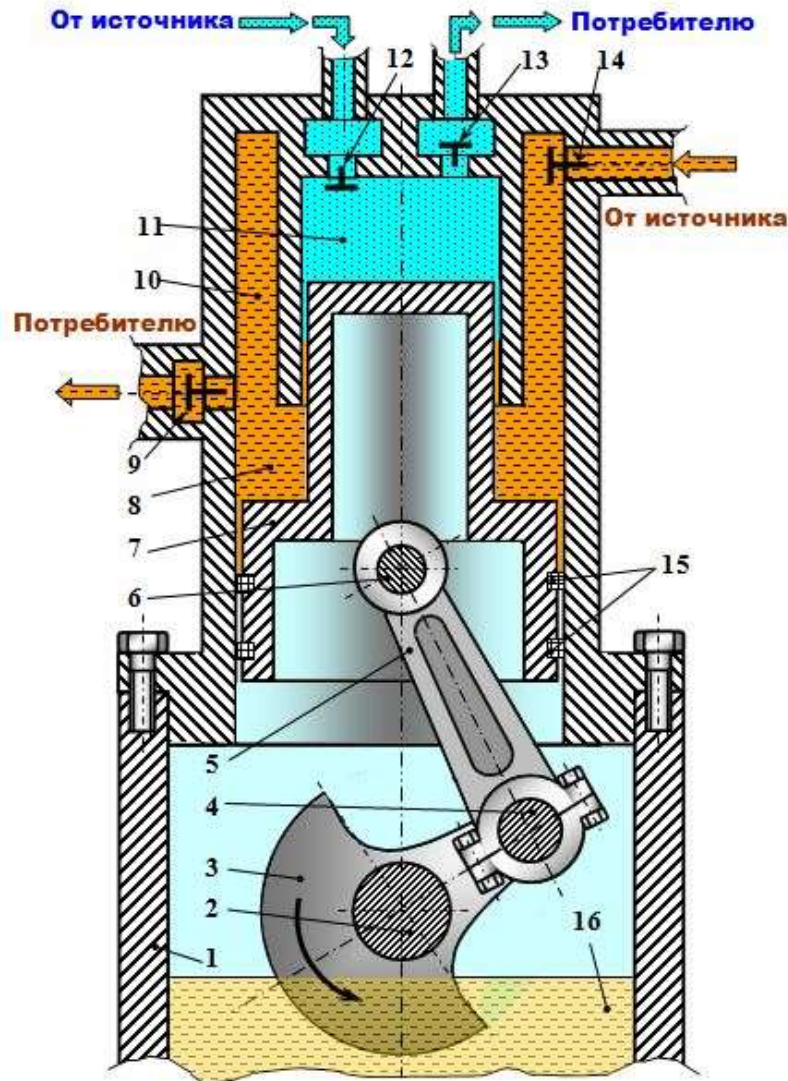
Схема поршневой бескрейцкопфной гибридной энергетической машины: 1 – картер; 2 – коленчатый вал; 3 – противовес; 4 – кривошип; 5 – шатун; 6 – шатунный палец; 7 – дифференциальный поршень; 8 – насосная полость; 9 – нагнетательный клапан; 10 – рубашка охлаждения; 11 – компрессорная полость; 12 – всасывающий клапан; 13 – нагнетающий клапан; 14 – всасывающий клапан; 15 – уплотнение; 16 – масло
